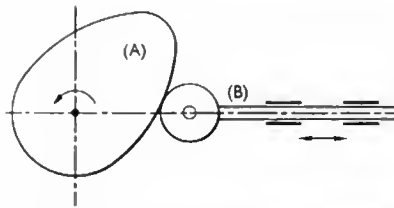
Came à galet; liaison unilatérale; (B) a un mouvement rectiligne alternatif
